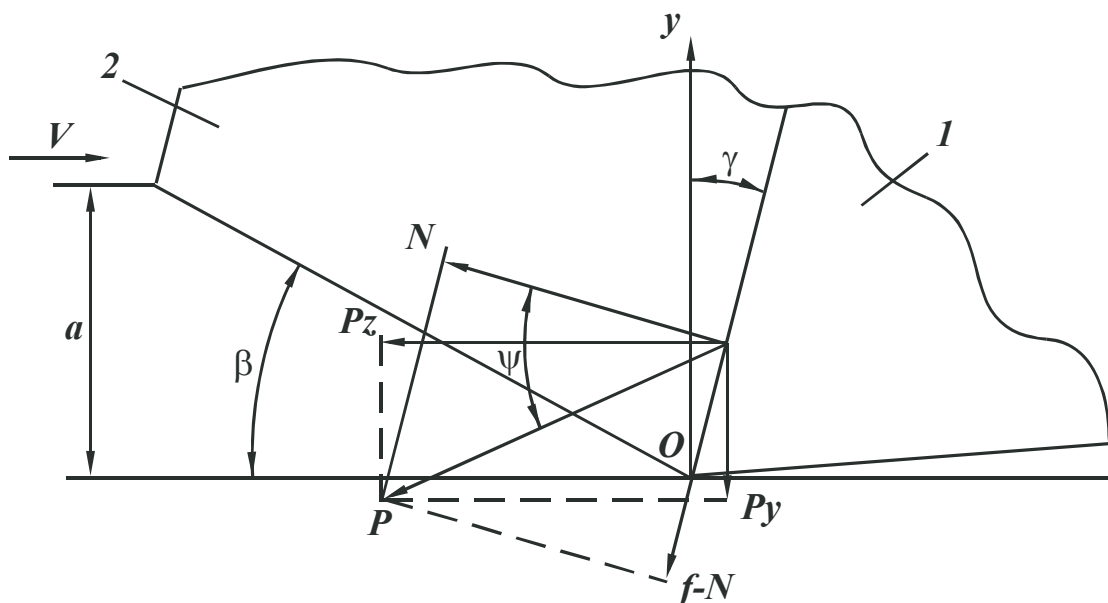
Расчетная схема процесса резания: 1-резец; 2-стружка.
